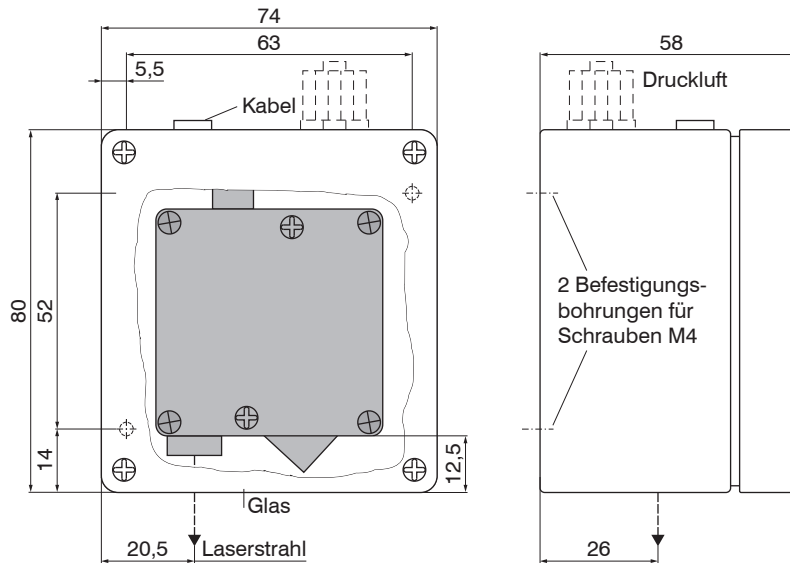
Schutzgehäuse für LD16x7 - 2/4/10/20
